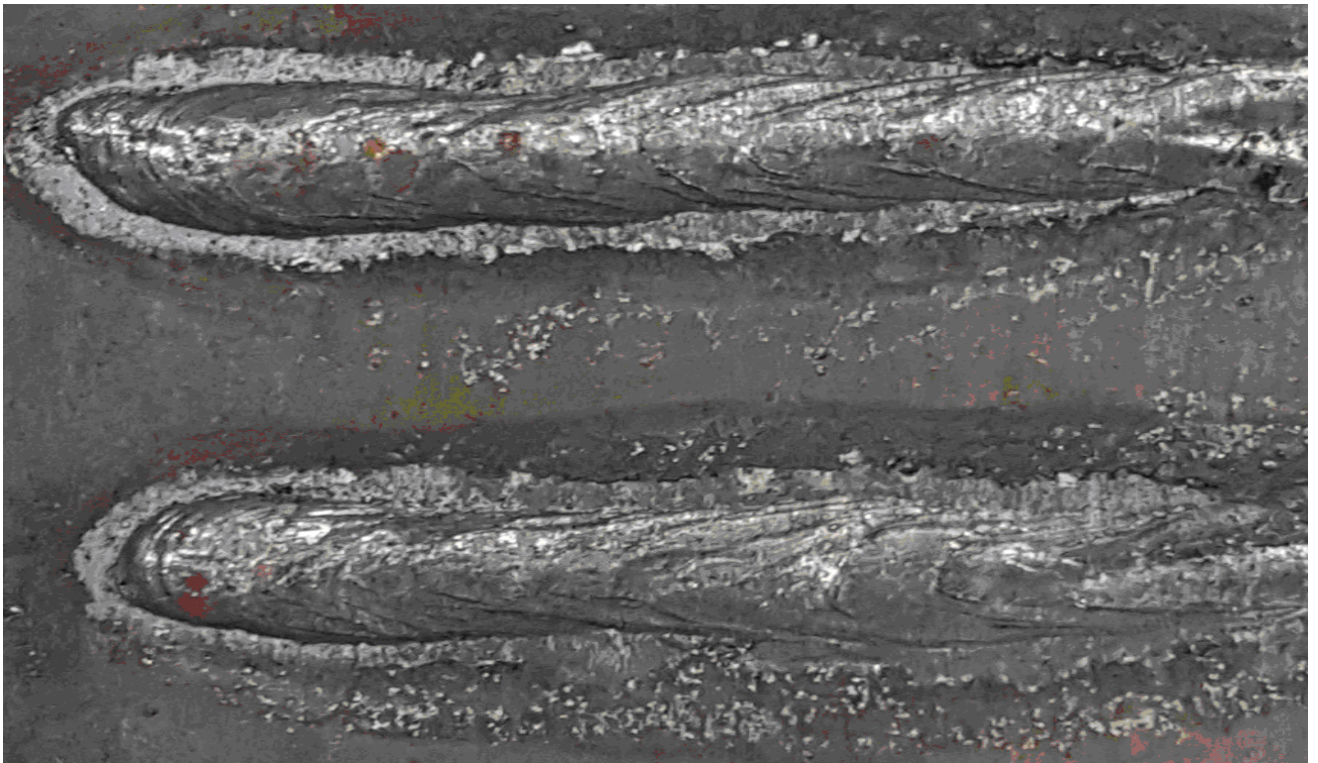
Внешний вид наплавки №3 (верхний шов) и №4 (нижний шов)
